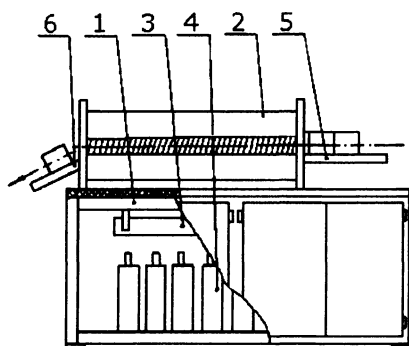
Схема кузнечного индукционного нагревателя типа КИН-500 конструкции МАЗ: 1 — каркас; 2 — индуктор; 3 — медная шина; 4 — конденсаторная батарея; 5 — механизм загрузки; 6 — лоток выгрузки
